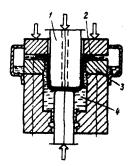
Схема штампа для гидромеханической вытяжки:
